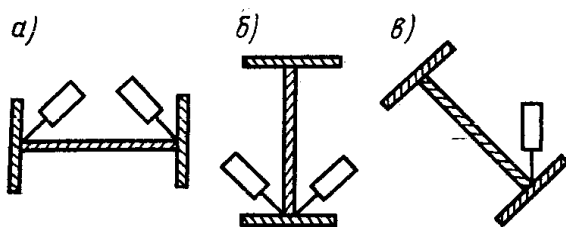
Способы укладки швов при сварке балок
